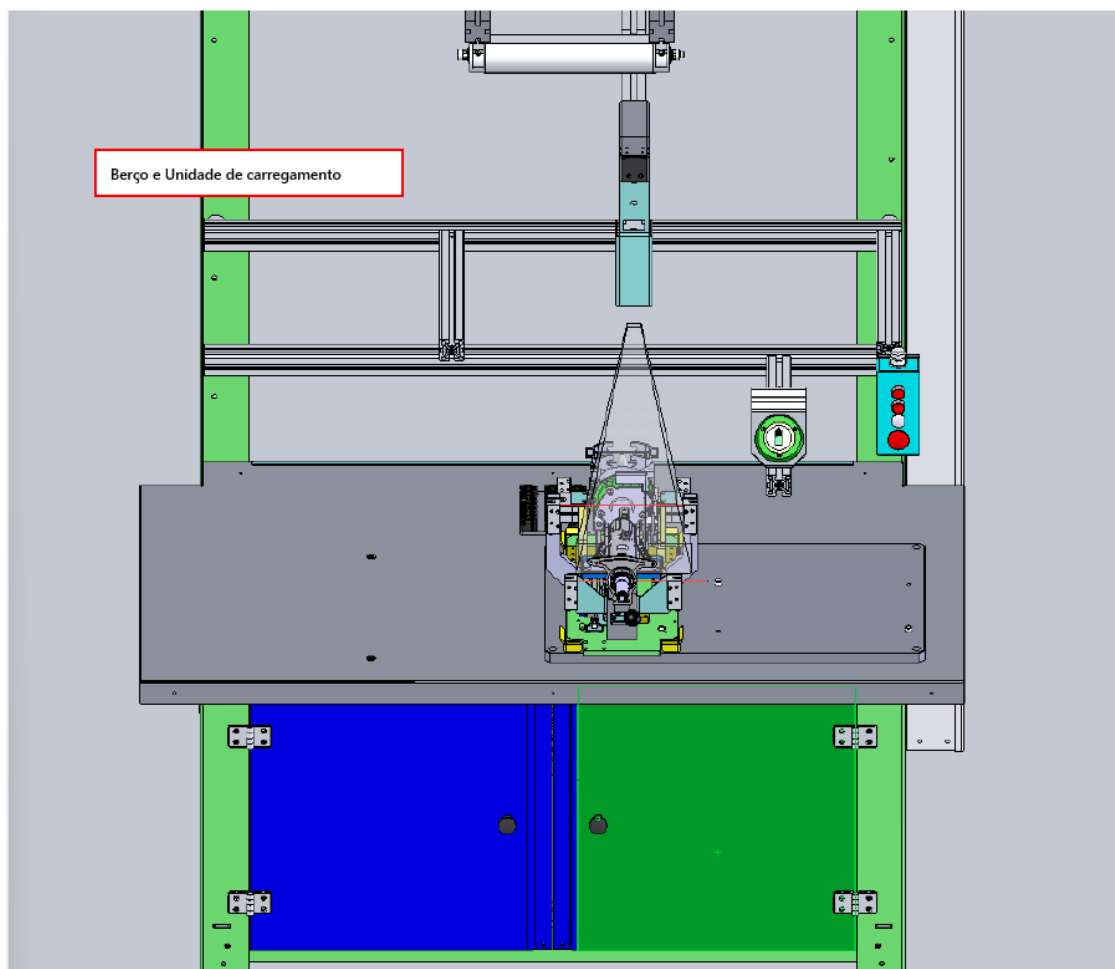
MÓDULO 09/19: INSPEÇÃO FINAL DA MONTAGEM DA MOLA
